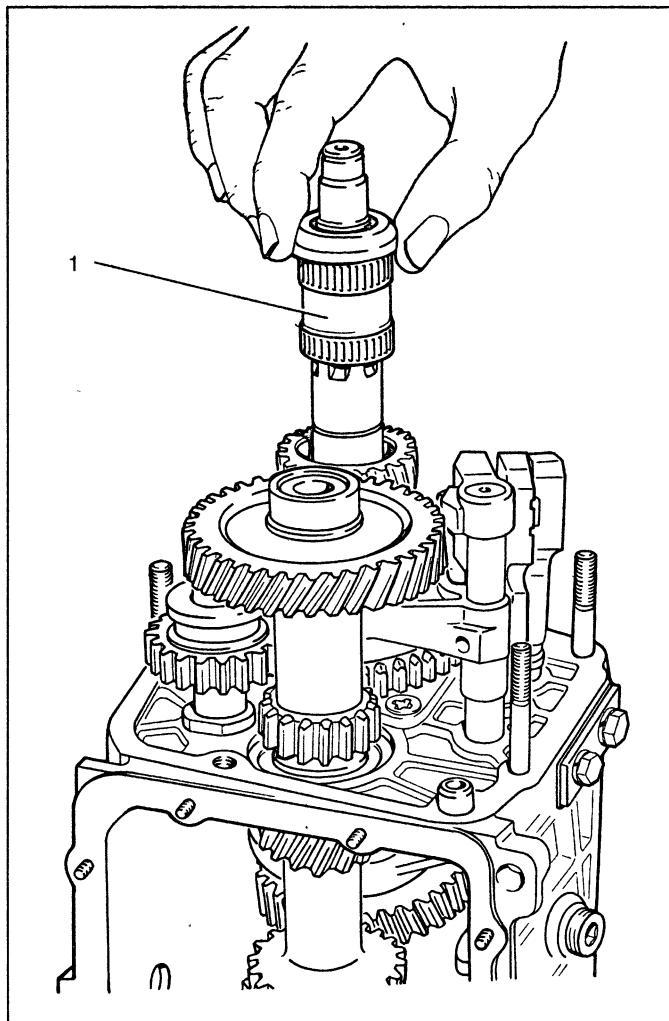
Снятие втулки шестерни V передачи: 1 – втулка
